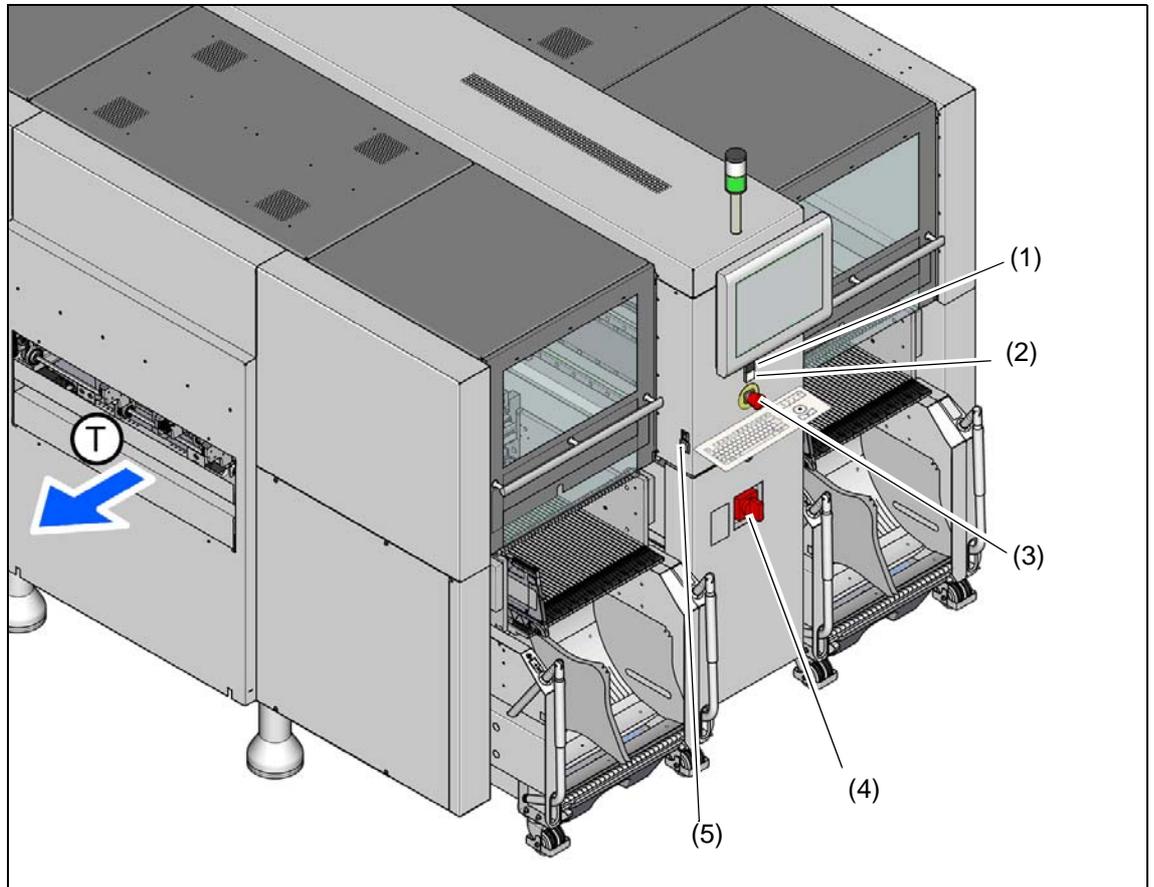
开关和按钮的位置 - PCB 输出侧视图 (示例为 SX4)
